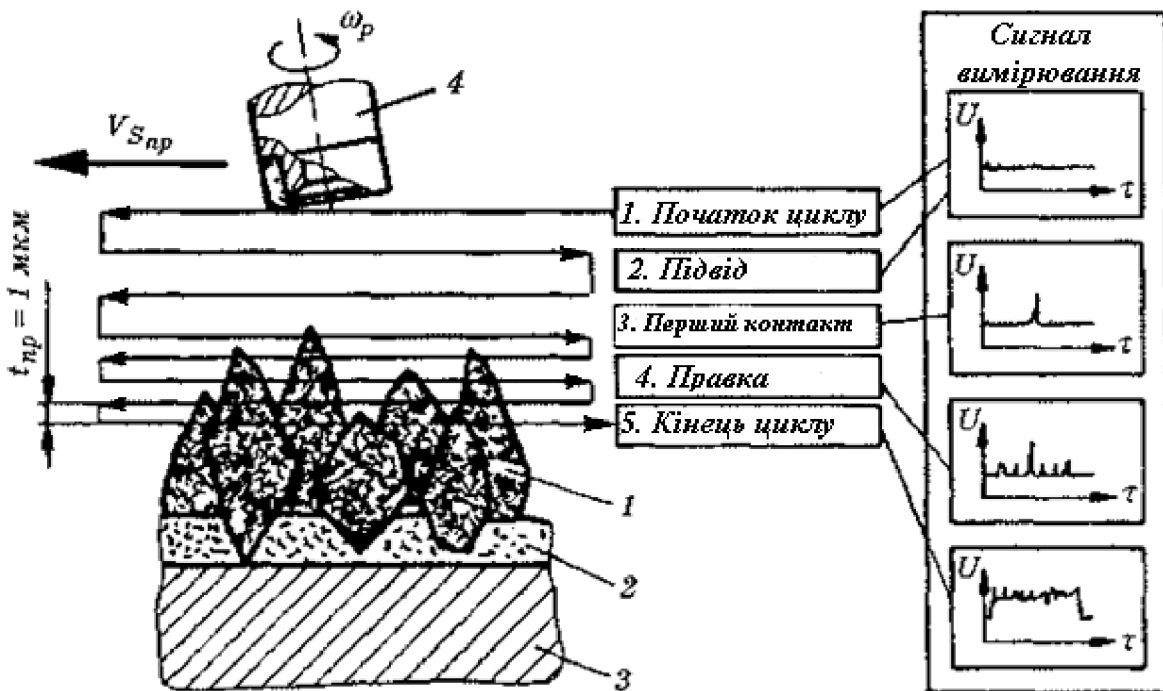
Схема правки алмазного (ельборового) круга на гальванічній звязці: 1 - зерна ельбора (алмаза); 2 - звязка; 3 - корпус круга; 4 - алмазний правильний круг.
